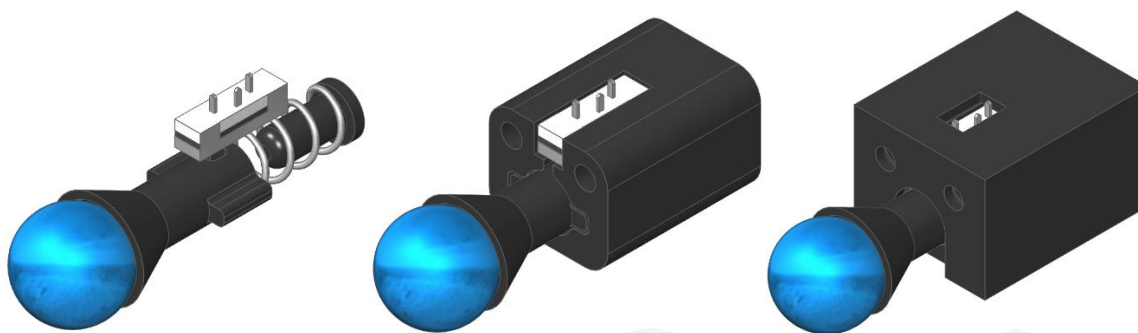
Protótipo do Conjunto de Sensores - Apalpador fixo.
